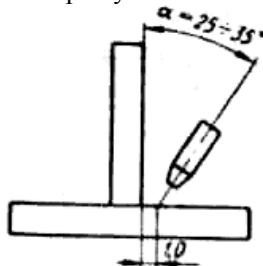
Положение горелки при автоматической дуговой сварке угловых швов
